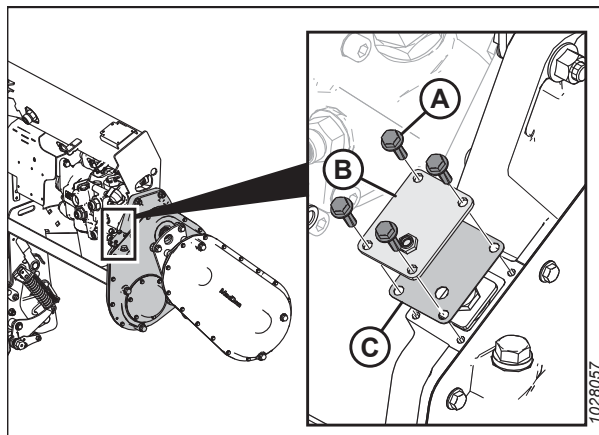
Hauptgetriebe mit Kettenspannerabdeckung
